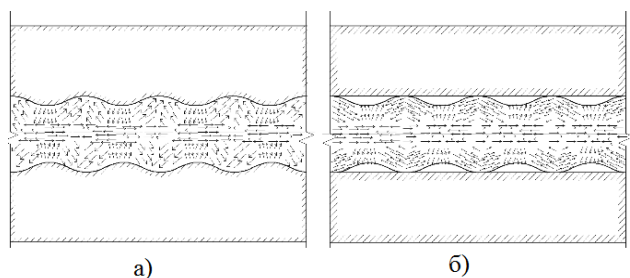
Движение макропотоков металла при обжатии на профильной (а) и гладкой (б) поверхностях штампа
